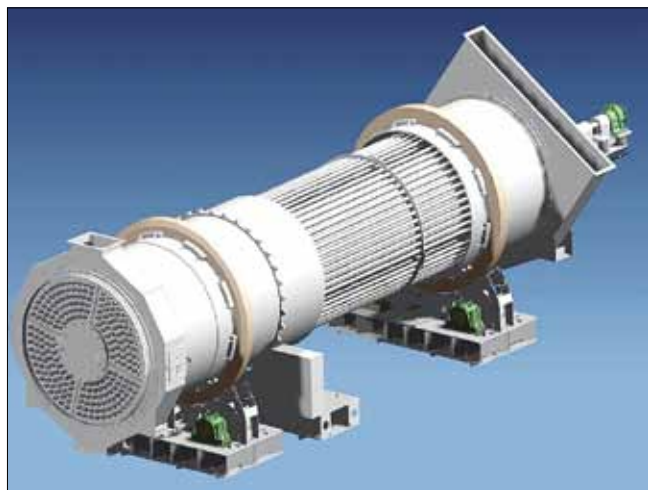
Вращающийся барабанный охладитель Claudius Peters типоразмера 290
